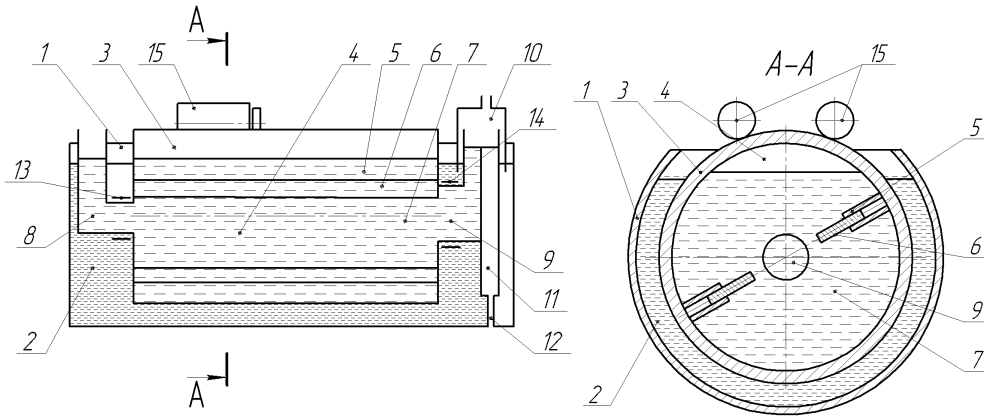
Метантенк: 1 – горизонтальний зовнішній корпус; 2 – рідина; 3 – циліндричний реактор; 4 – камера зброджування; 5 – перегородка; 6 – рухома пластина; 7 – органічна маса; 8 – патрубок для підводу органічної маси; 9 – патрубок для відводу органічної маси; 10 – патрубок для відводу біогазу; 11 – вивантажувальна камера; 12 – патрубок для вивантаження органічної маси; 13, 14 – підшипникові вузли; 15 – зовнішній привід.
